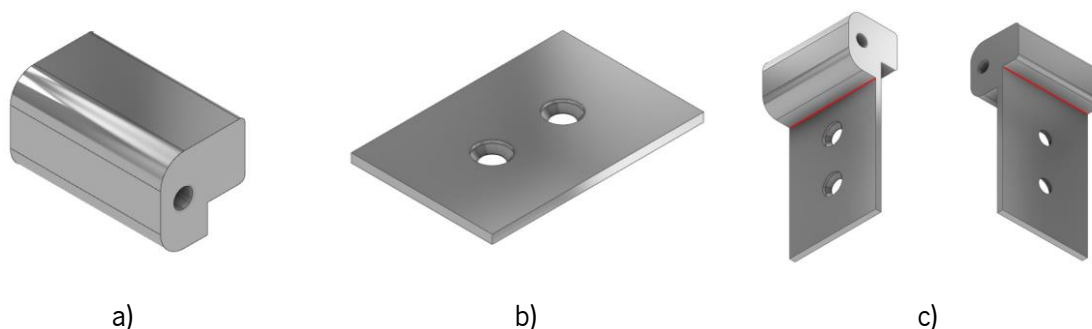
Perfil do fixador da dobradiça da porta de segurança extrudido, chapa do fixador maquinada e soldadura para união de ambas geometrias, respetivamente em a), b) e c).
